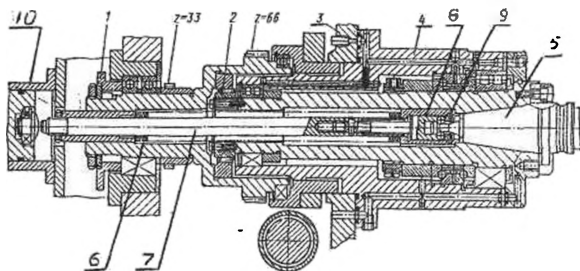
Шпиндельний вузол БВ IP500МФ4:
